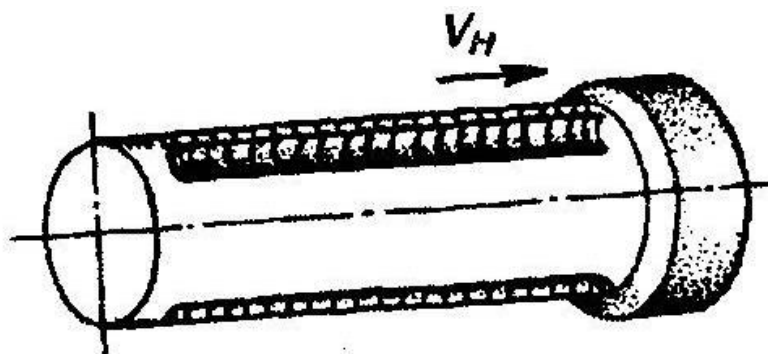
Восстановительная наплавка вала по образующим
